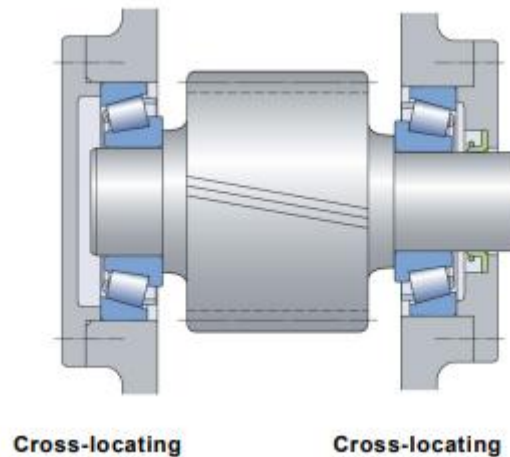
Disposição dos rolamentos em arranjo cruzado, "cross locating arrangement" [46]
